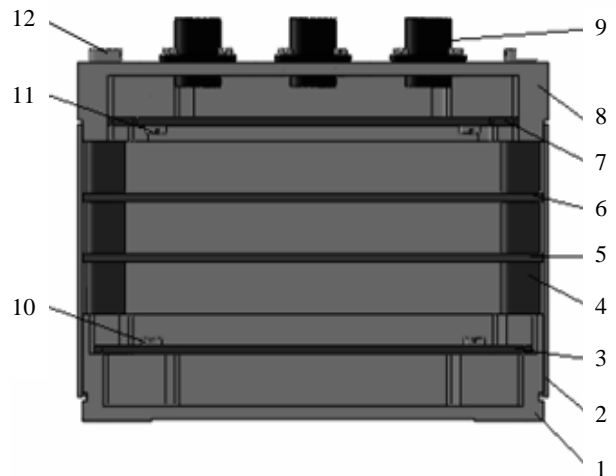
Общий вид типовой конструкции бортовых приборов: 1 – нижняя панель; 2 – кожух; 3, 5–7 – платы; 4 – втулка; 8 – верхняя панель; 9 – соединитель; 10, 11 – винт малого диаметра; 12 – общий винт
